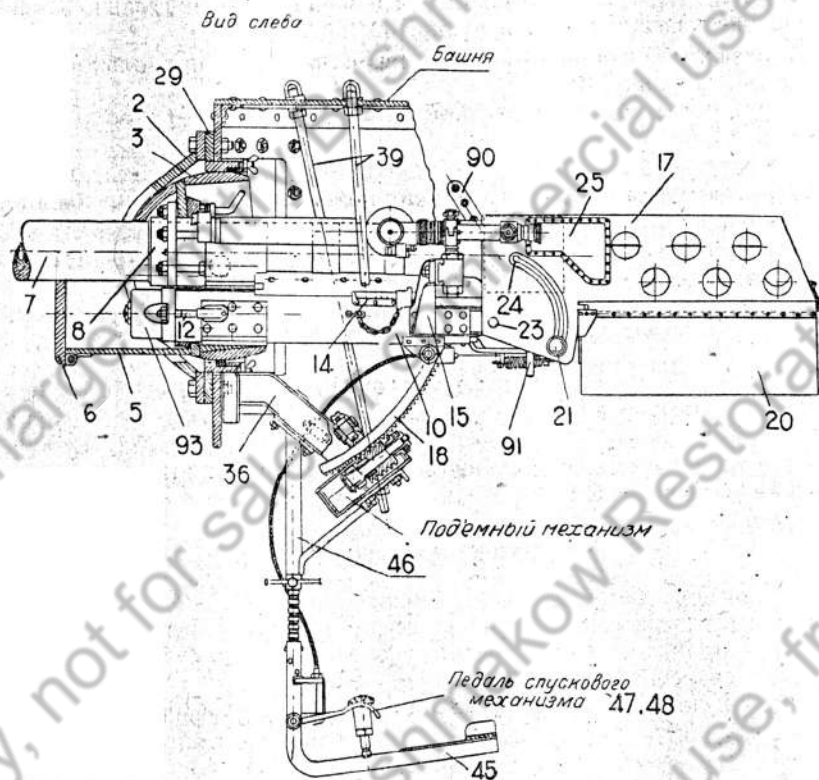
Общий вид (разрез) спаренной установки пушки и пулемета.
